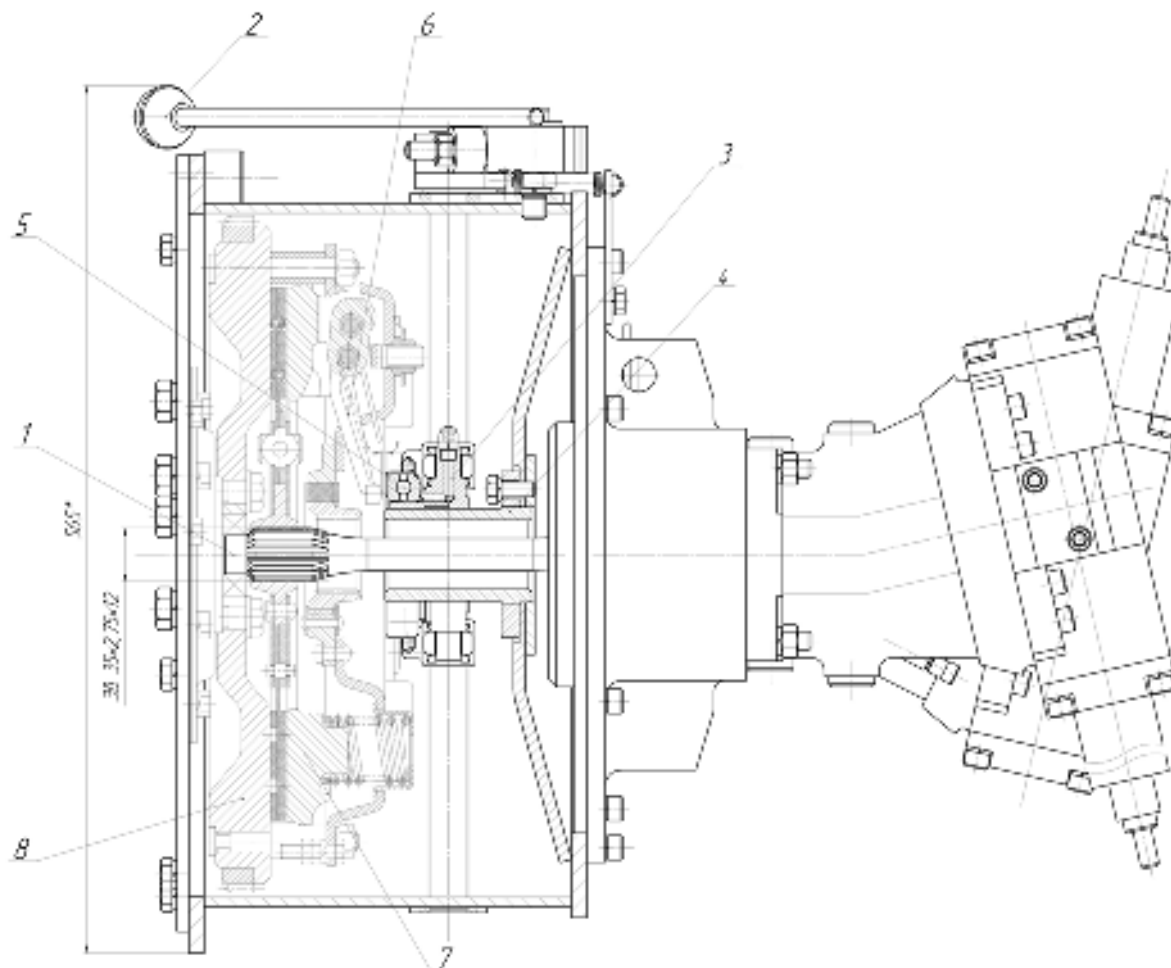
Установка муфты сцепления и насосного агрегата
